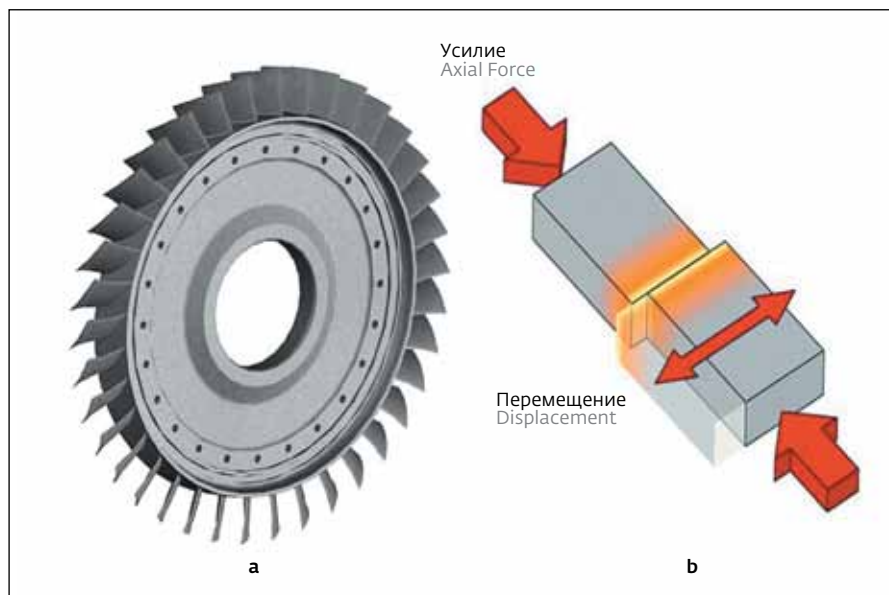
Рабочее колесо компрессора в конструктивном исполнении: моноколесо (а) и схема процесса линейной сварки трением (б)
